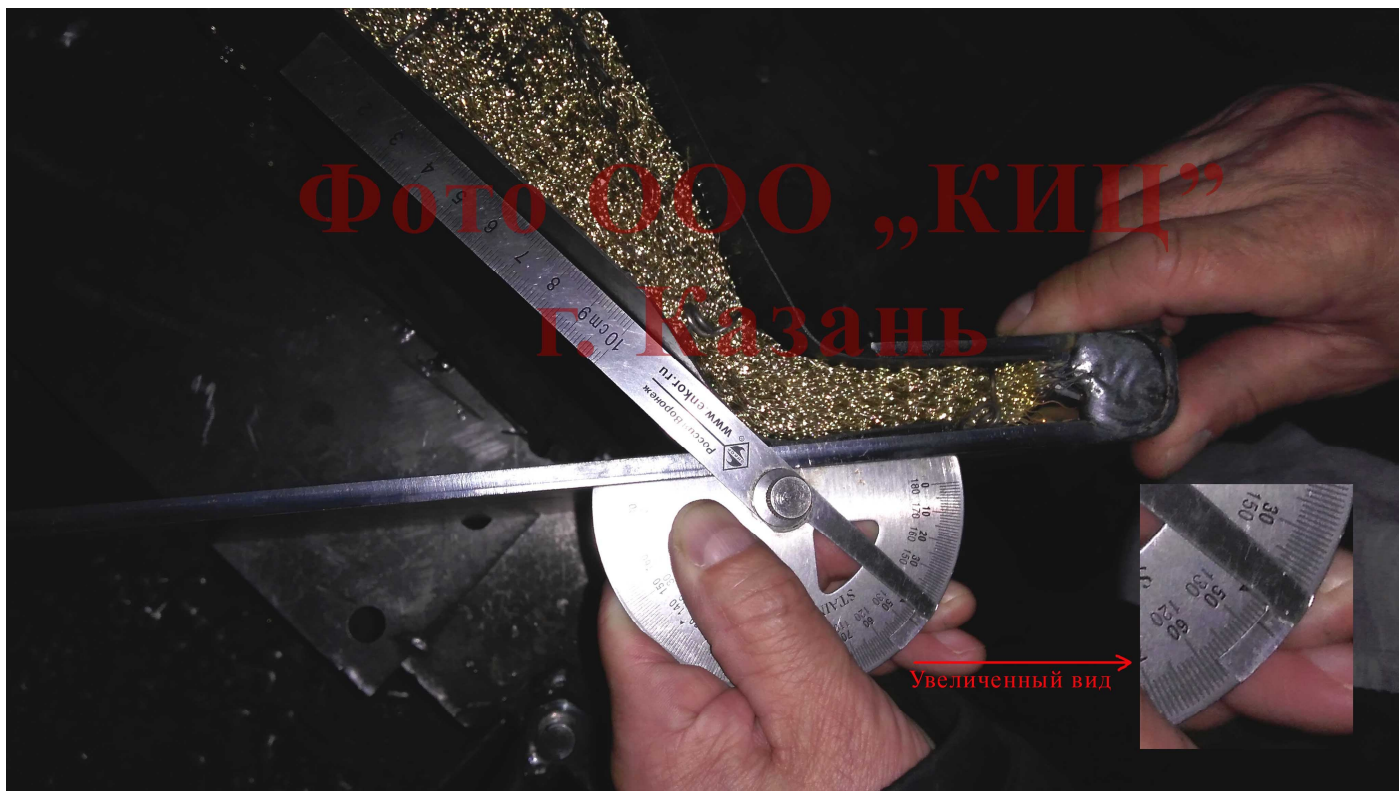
Угол сгиба задней пластины - 132 градуса (до испытаний)
